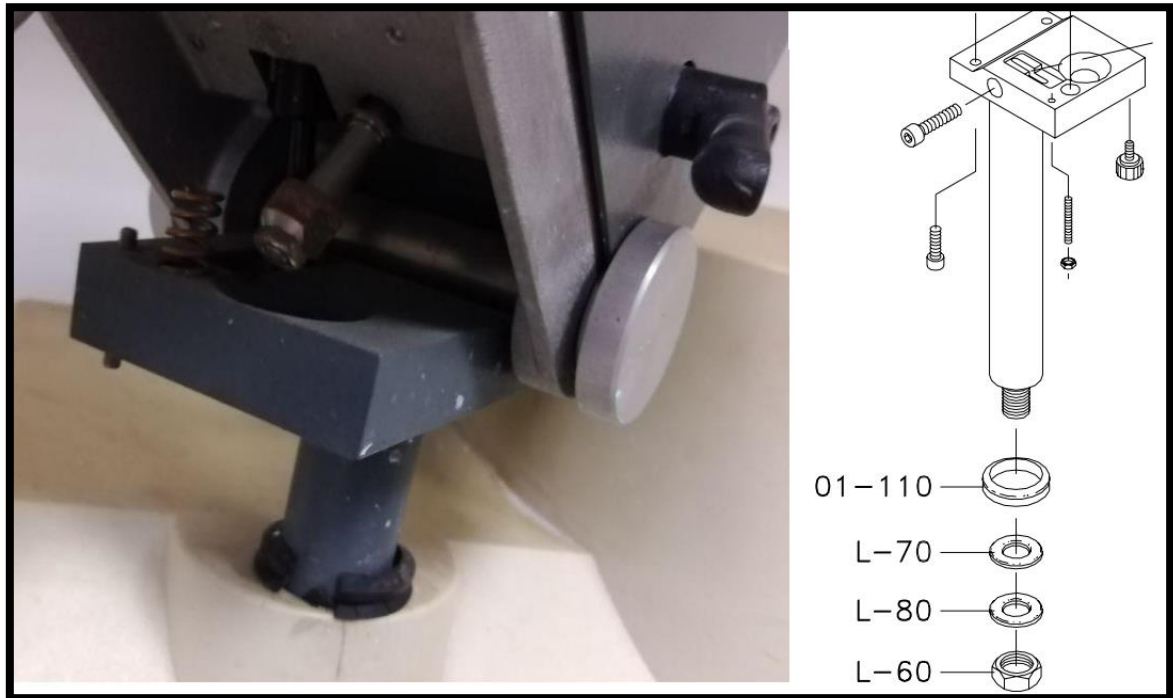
Elemento de unión LABOFORCE-3 con la pulidora (Izquierda, Fuente: Propia). Detalle del elemento de unión (derecha, Fuente: www.struers.com)
